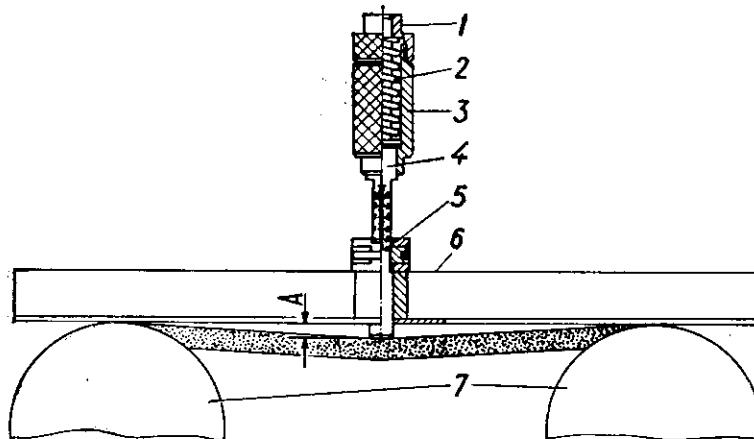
Приспособление 4905-3924100 для определения прогиба ремней:
